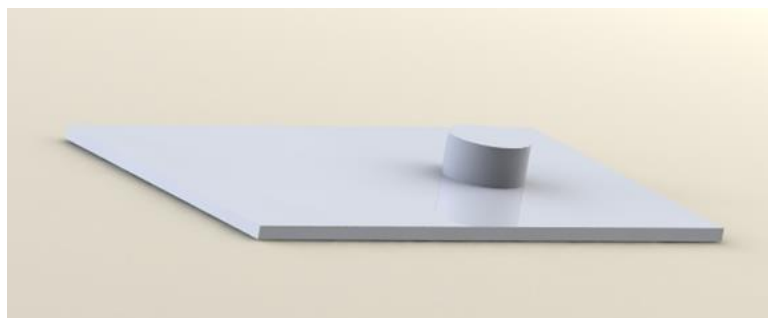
Desenho 3-D do molde em acrílico com dimensões da câmara cilíndrica de reação de 3 mm de diâmetro e de altura.
